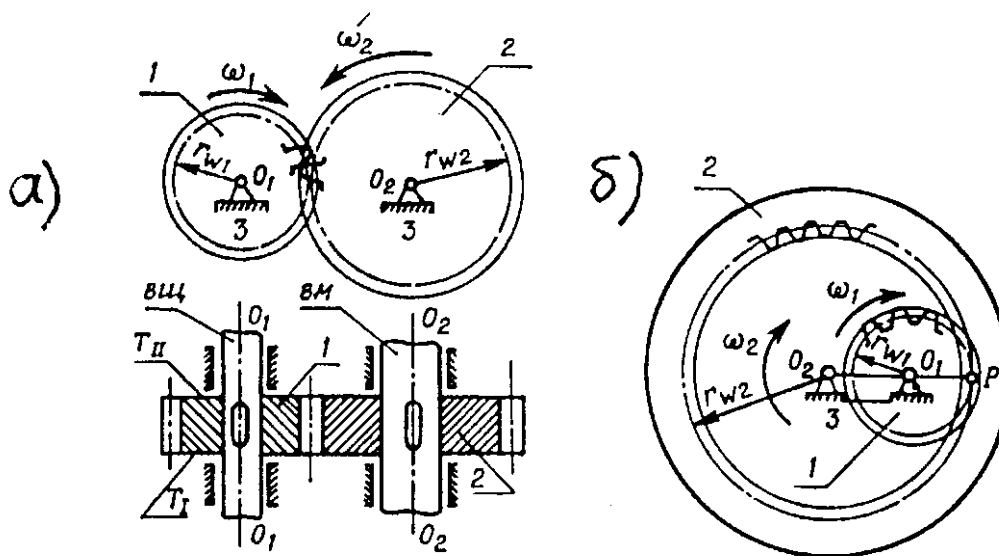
Кинематические схемы простой цилиндрической зубчатой передачи
